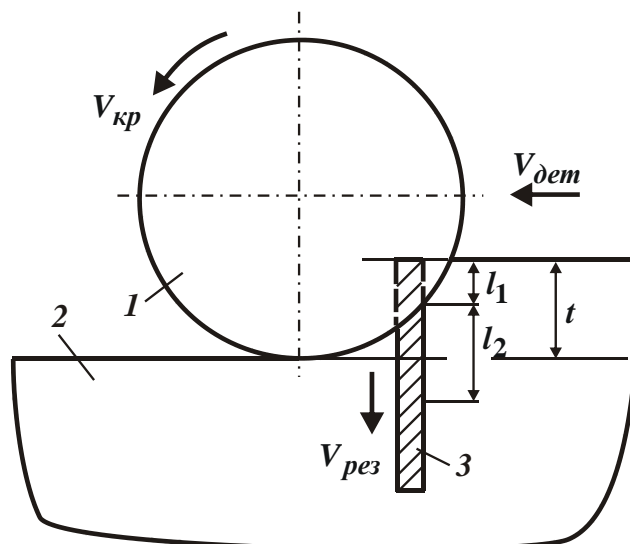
Расчетная схема процесса шлифования: 1 – шлифовальный круг; 2 – обрабатываемая деталь; 3 – адиабатический стержень.
